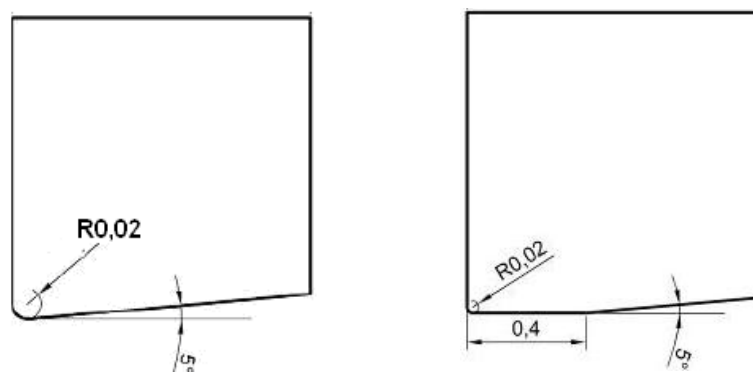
Esquema bidimensional de la herramienta sin desgaste y con desgaste de flanco 0.4mm. [1].
